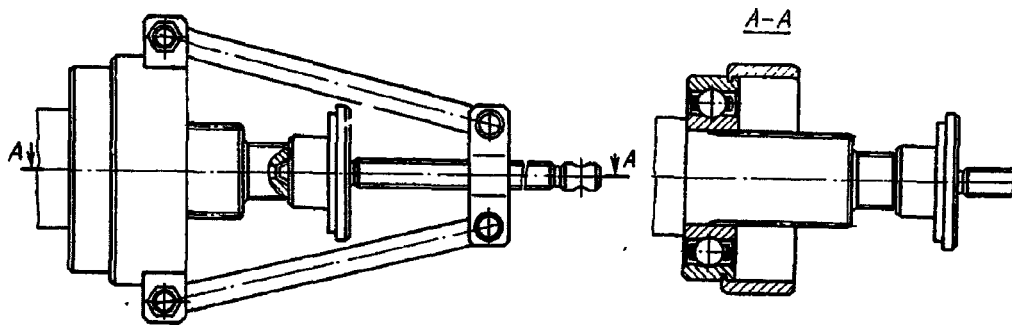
Снятие подшипника зубчатого колеса привода заднего моста
